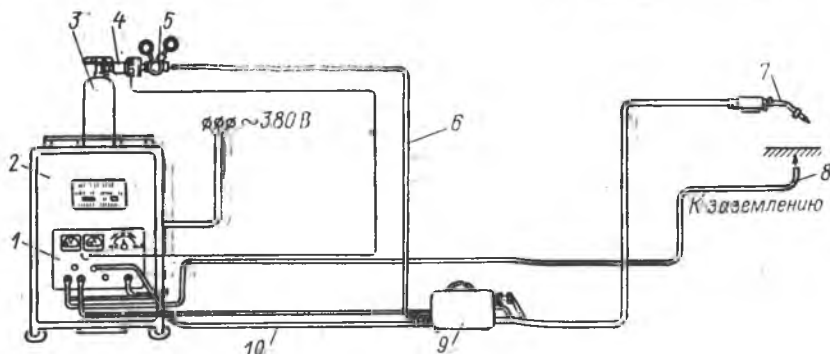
Схема полуавтоматической установки для сварки тонколистовых металлов в углекислом газе.
